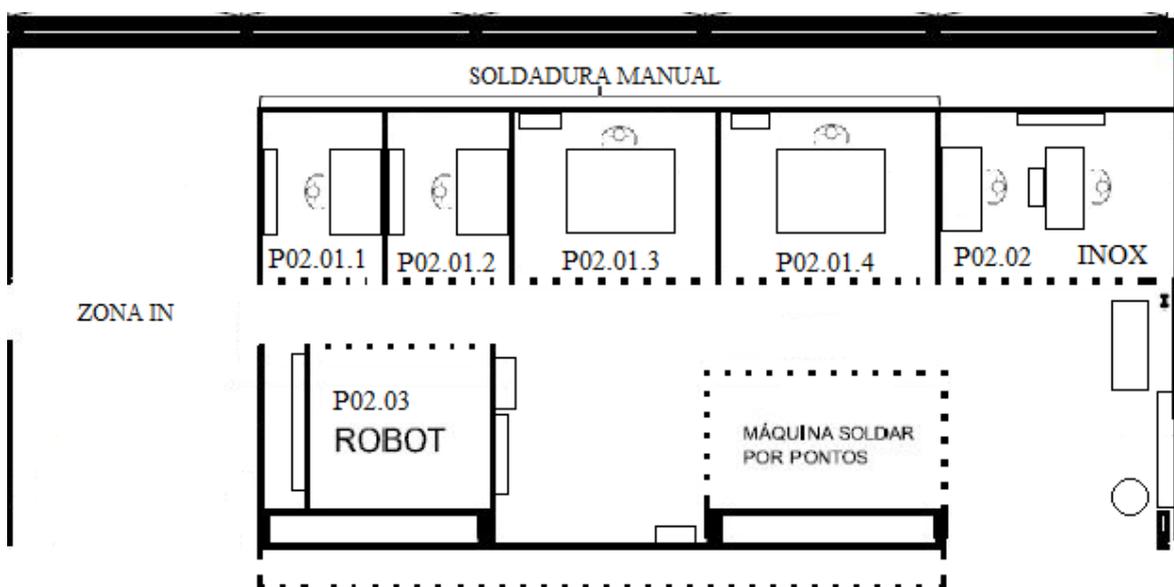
Layout da linha de soldadura (adaptado Schmitt)
